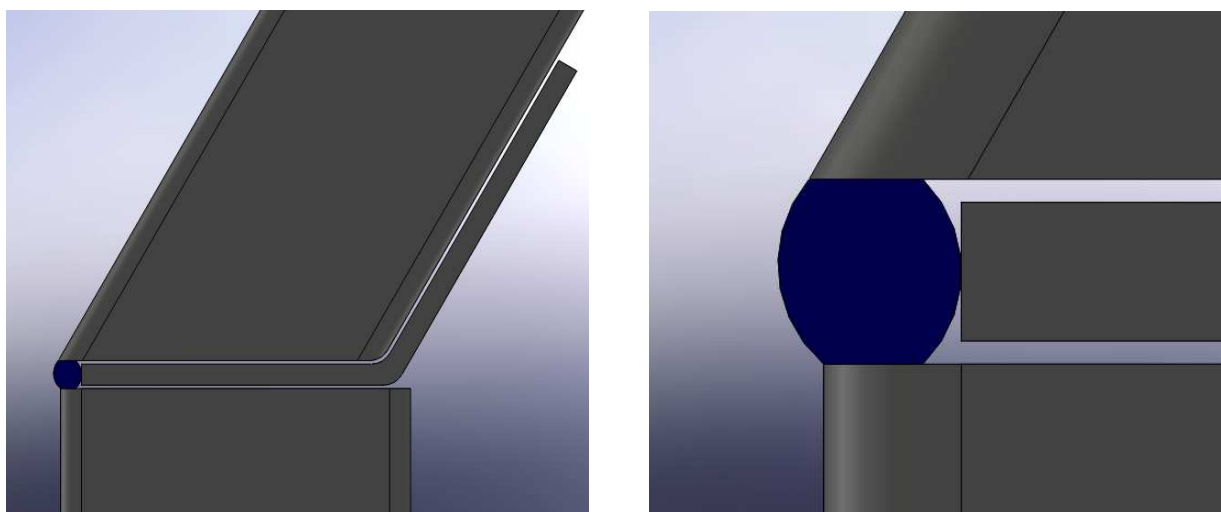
Pormenor do defeito de soldadura referido
